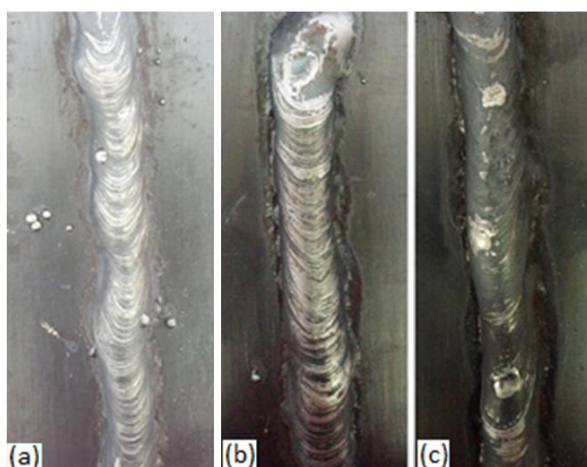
(a) amostra 1, (b) amostra 2, (c) amostra 3, após a soldagem
